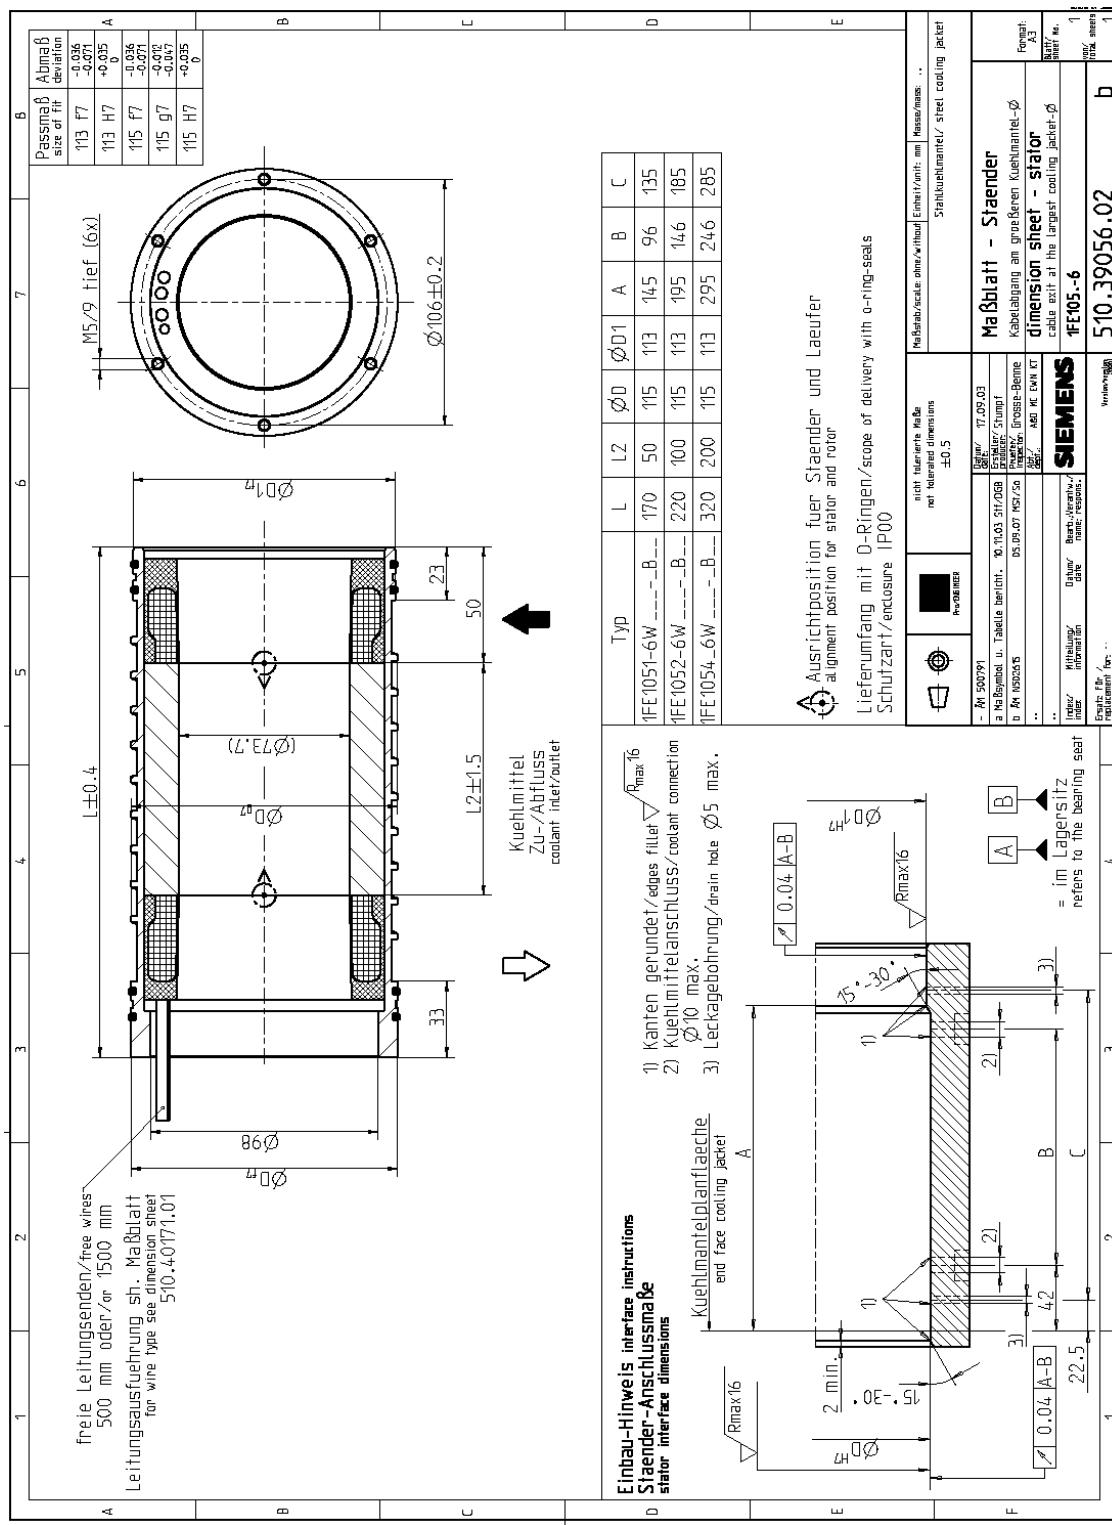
1FE105□-6, Ständer mit Kühlmantel, Kabelabgang am größeren Kühlmanteldurchmesser
